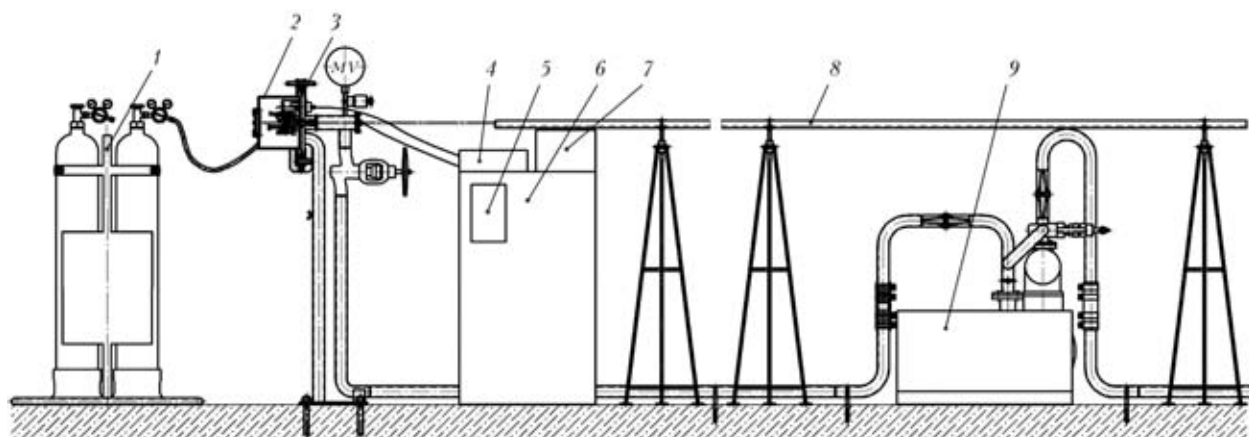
Схема стенда для сварки GTAW стыкозамковых соединений ПЭЛов: 1 — стойка газобаллонная; 2 — сварочная камера; 3 — головка сварочная АДЦ 627.03.00.000; 4 — коллектор АДЦ 625.07.00.000; 5 — пульт управления выносной ИЦ 616.30.00.000; 6 — источник питания ИЦ 616.У3.1; 7 — блок контроллера ИЦ 616.20.00.000; 8 — ложемент; 9 — агрегат вакуумный золотниковый
